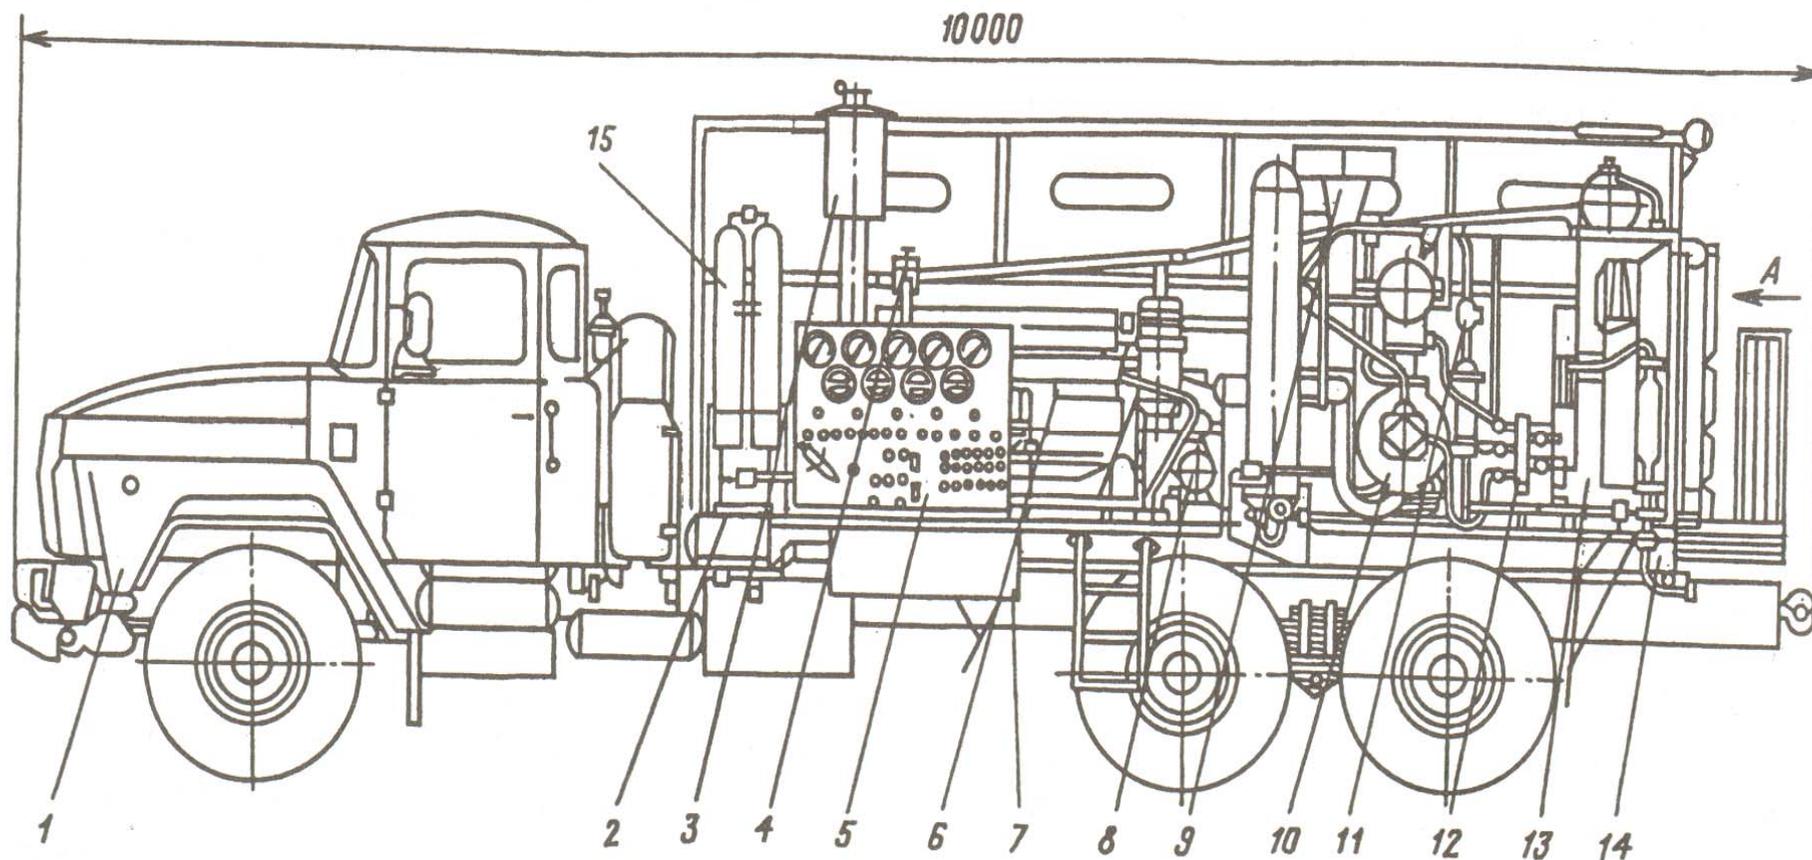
Азотная компрессорная станция на базе компрессора СД-9/101М:
